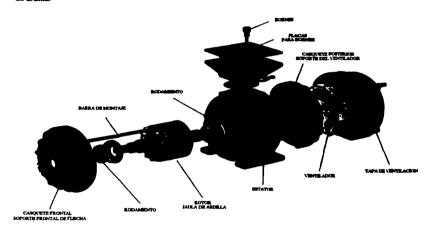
Detalles de construcción de un motor típico jaula de ardilla. •
